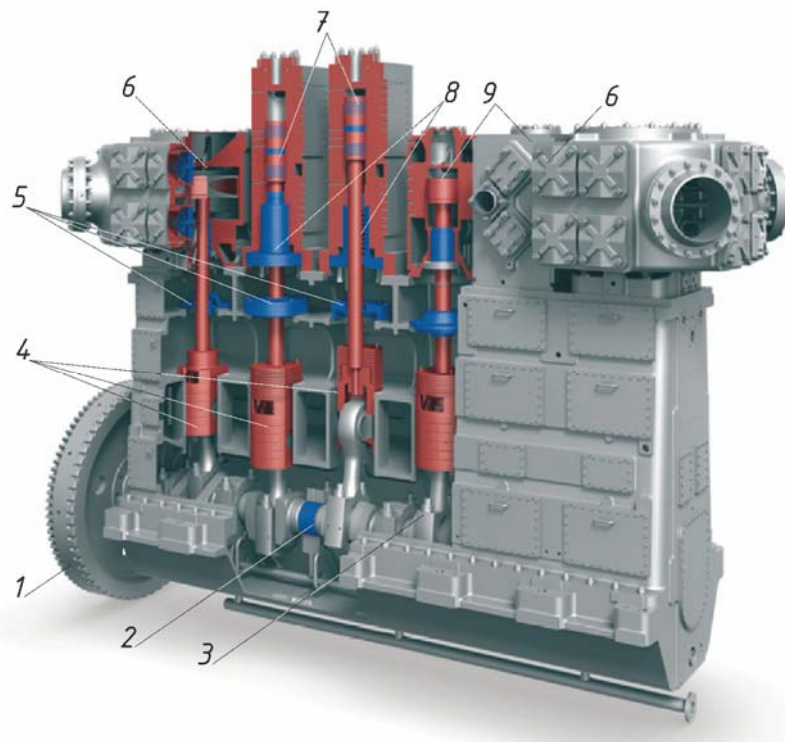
Загальний пристрій газового компресора серії 6LP250-5S-1 фірми Cryostar: 1 – маховик та фланець приводу; 2 – колінчастий вал; 3 – шатун; 4 – повзун; 5 – ущільнення штока; 6 – циліндри першого ступеня; 7 – циліндри четвертої і п'ятої ступіні; 8 – ущільнення штоків; 9 – циліндри другого ступеня
